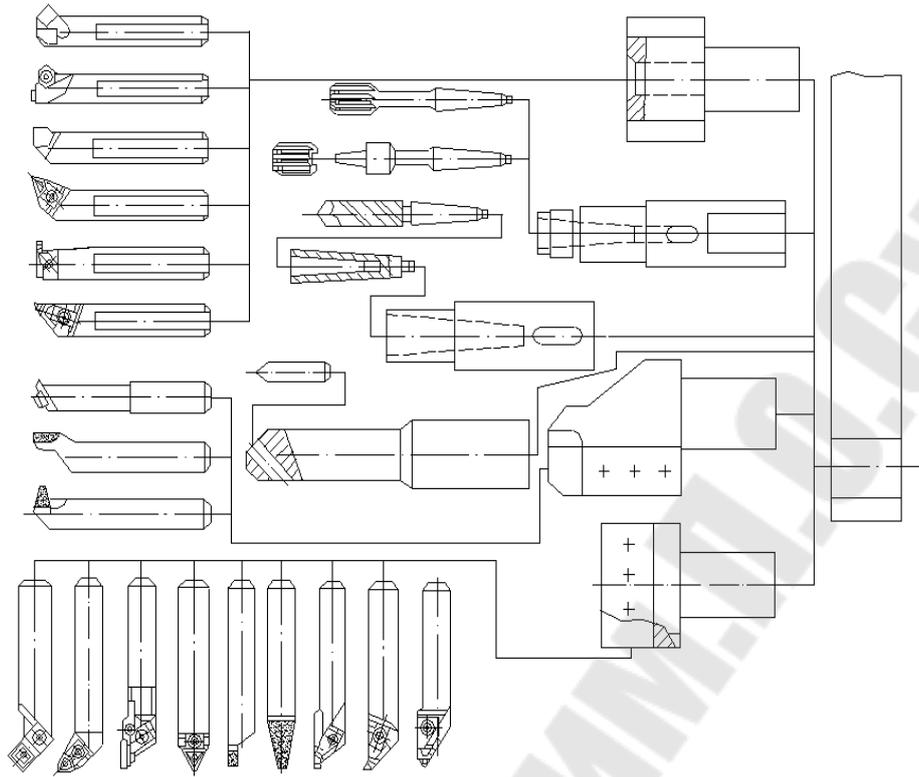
Комплект режущего инструмента для токарного станка с УЧПУ модели 1740РФ3
